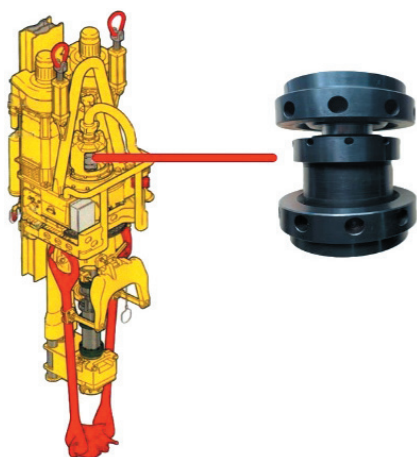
Внешний вид верхнего привода и ПТ в сборе
